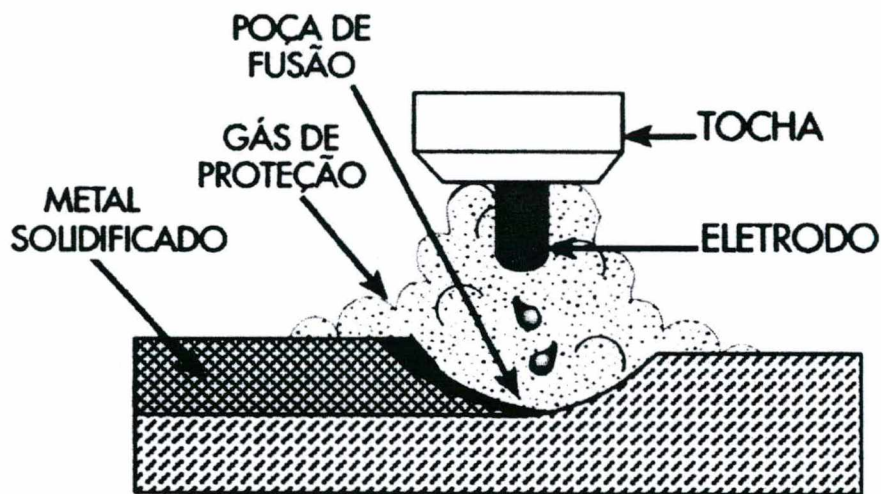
Processo de soldagem a arco voltaico com atmosfera gasosa.
